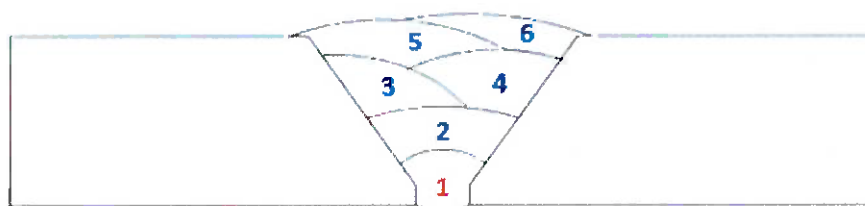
Esquema da junta soldada indicando as camadas e os passes de solda
